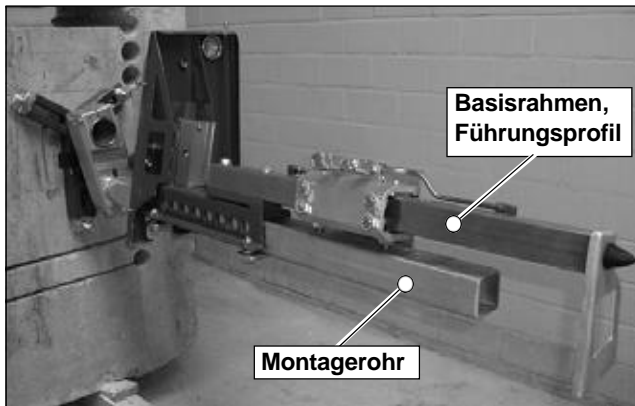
Schwenkgelenk, Montagerohr auf dem CSA•100 Präzisions-Schwenkfuß ausrichten
